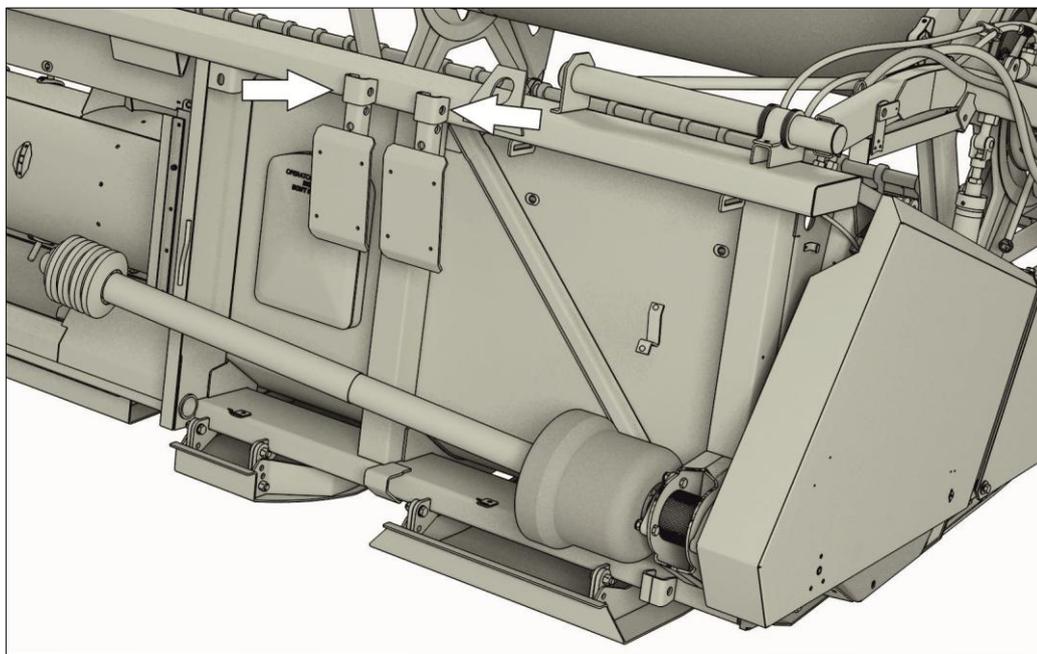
Установка опор при рабочем положении жатки
